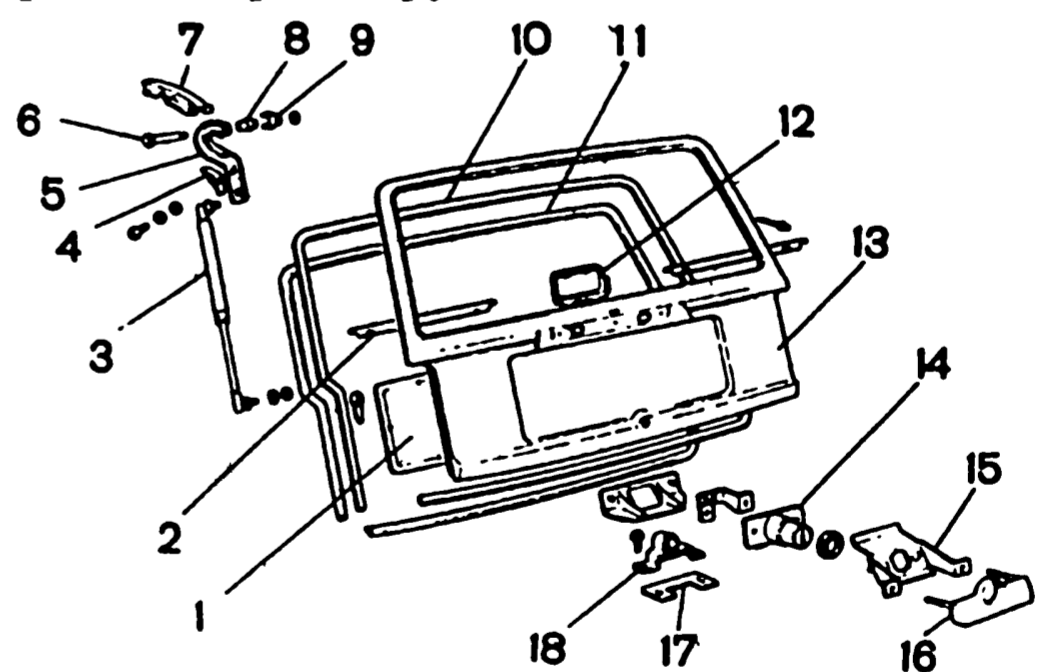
Дверь задка автомобиля ВАЗ-2104: 1 - обивка двери; 2 - держатель обивки; 3 - упор двери задка с шарнирами; 4 - усилитель звена петли; 5 - звено петли двери; 6 - болт петли; 7 - кронштейн петли; 8 - втулка оси; 9 - кронштейн втулки; 10 - прокладка уплотнителя двери; 11 - уплотнитель проема двери; 12 - облицовка моторедуктора; 13 - дверь задка в сборе; 14 - замок двери; 15 - кронштейн крепления замка; 16 - ручка двери; 17 - регулировочная прокладка фиксатора; 18 - фиксатор замка двери
